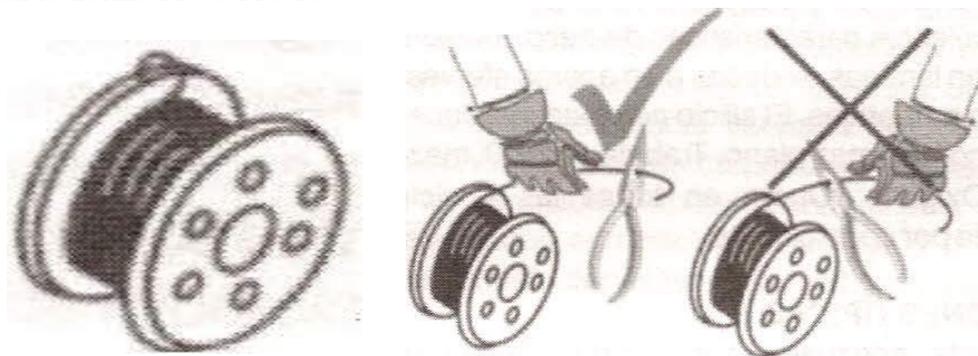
Montaje de carretes de soldadura Mig (Tomada por el catálogo de productos de soldadura WEST - ARCO).
